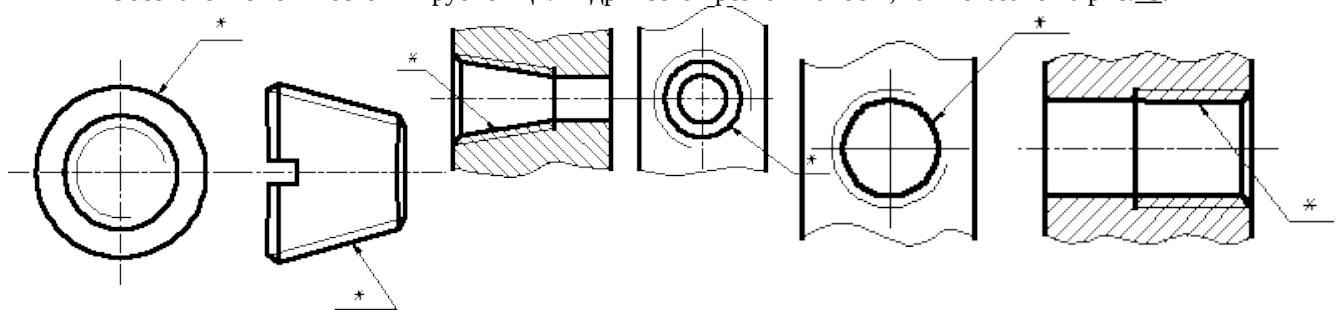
Пример обозначения конической и трубной цилиндрической резьб
